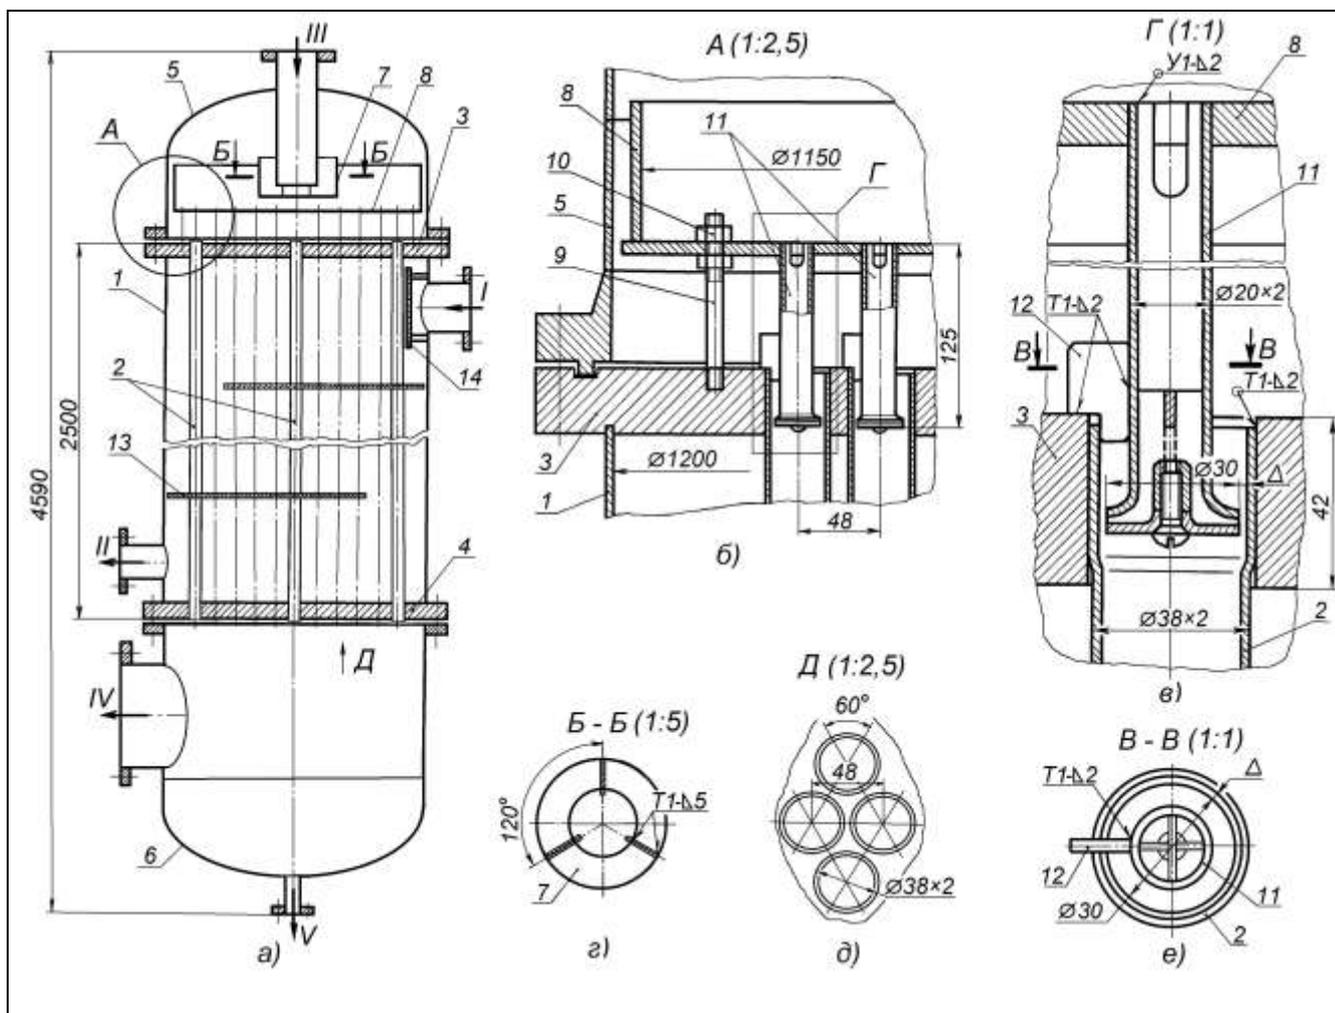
Кожухотрубчатый вертикальный вакуумный пленочный испаритель: а) – общий вид; б) – схема установки распределительной тарелки 8 на верхней трубной решетке 3 с помощью шпилек 9 с гайками 10; в, е) – схемы установки пленкообразователя 11 внутри теплообменных труб 2 приваркой фиксирующей пластины 12 к трубной решетке 3; г) – схема закрепления гидрозатвора 7 на штуцере подачи кубовой жидкости; д) – схема размещения труб 2 на трубных решетках 3 и 4. Поток: I – вход греющего водяного пара; II – выход конденсата водяного пара; III – вход кубовой жидкости; IV – выход пара кубовой жидкости; V – штуцер для дренажа (опорожнения) кубовой жидкости
